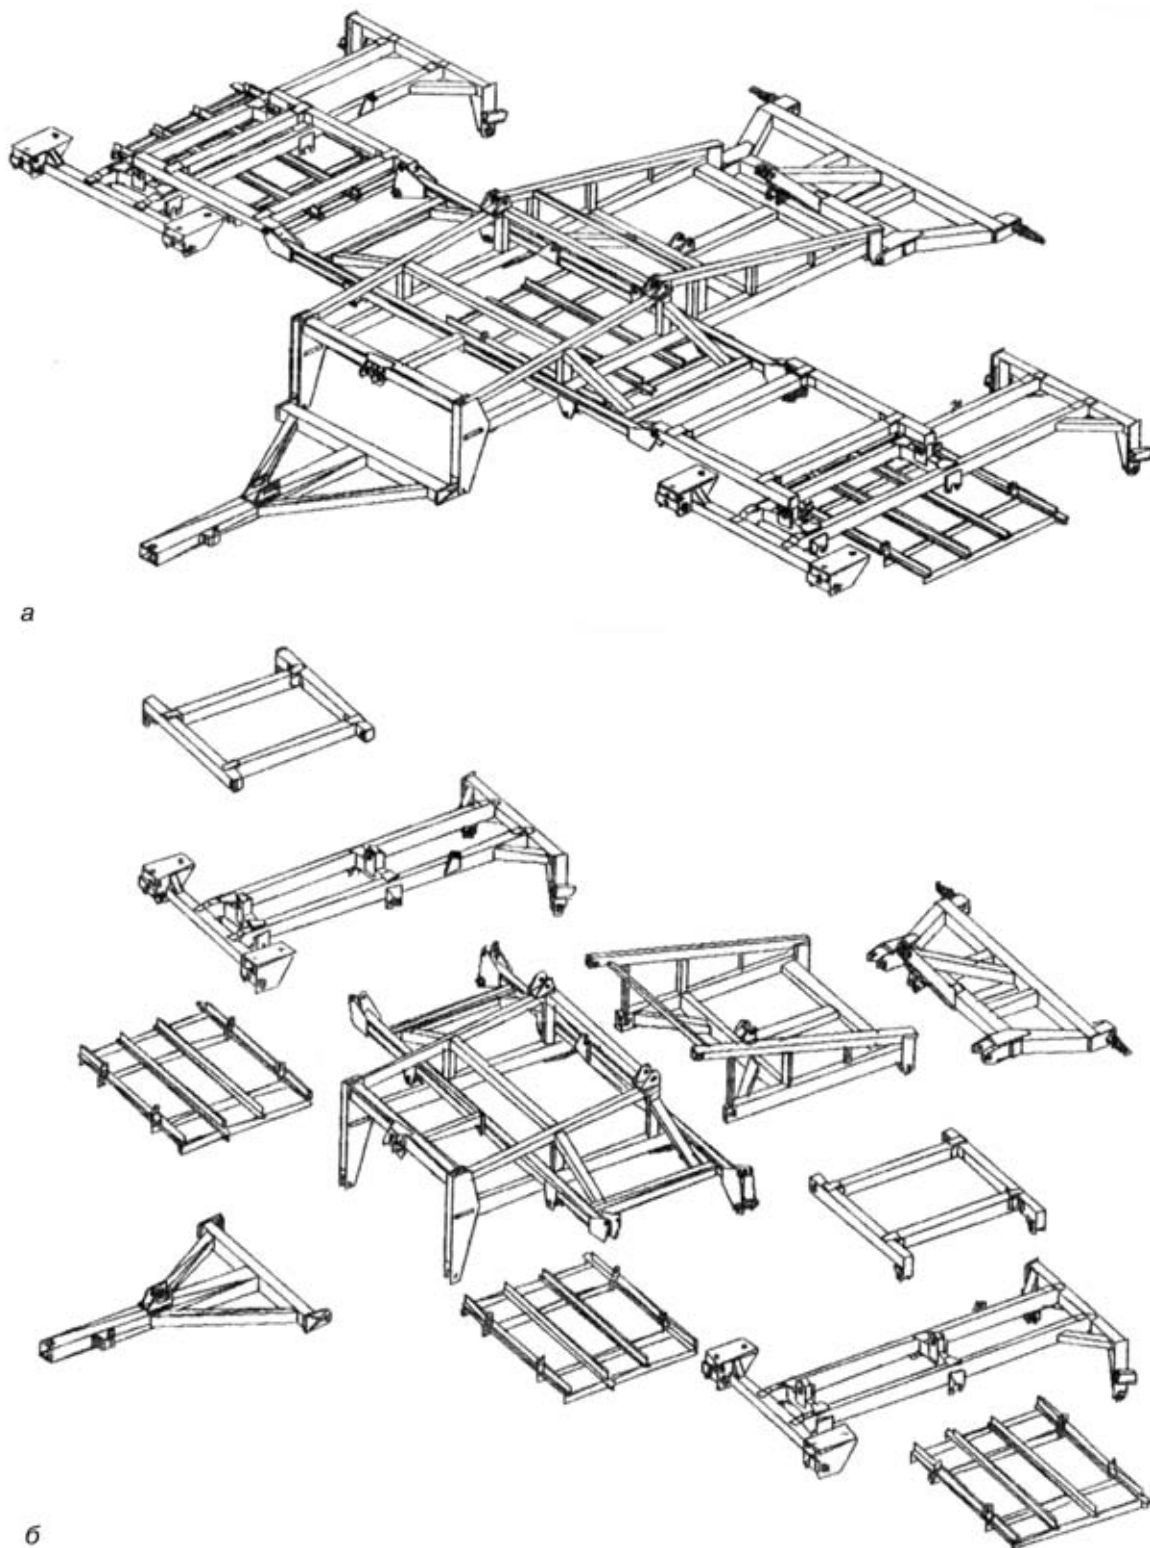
Оснащаемые сварные конструкции: *а* — рабочее положение; *б* — схема сборки
